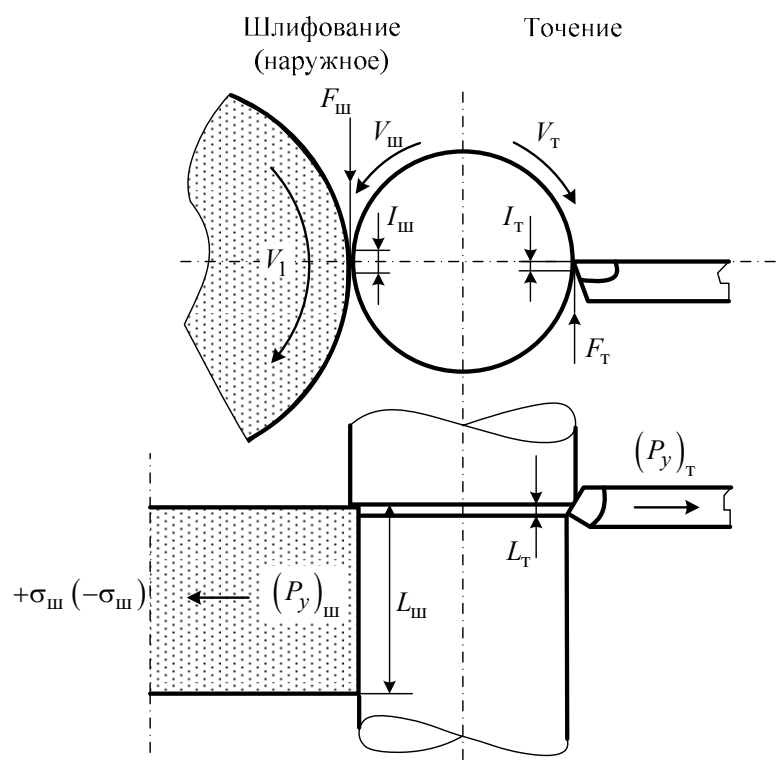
Схема контакта инструмента с обрабатываемой поверхностью при шлифовании и точении:
